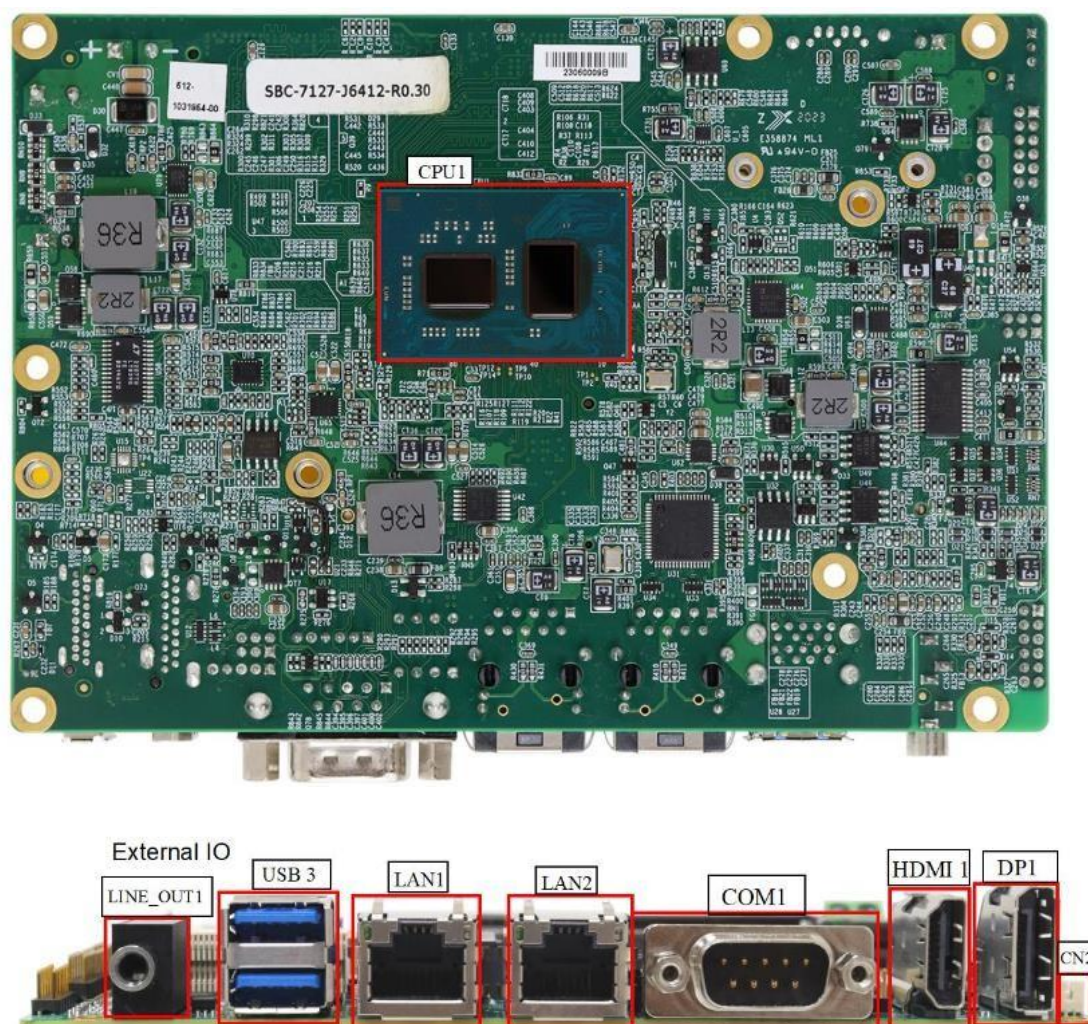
Jumper und Anschluss – Board Rückansicht
